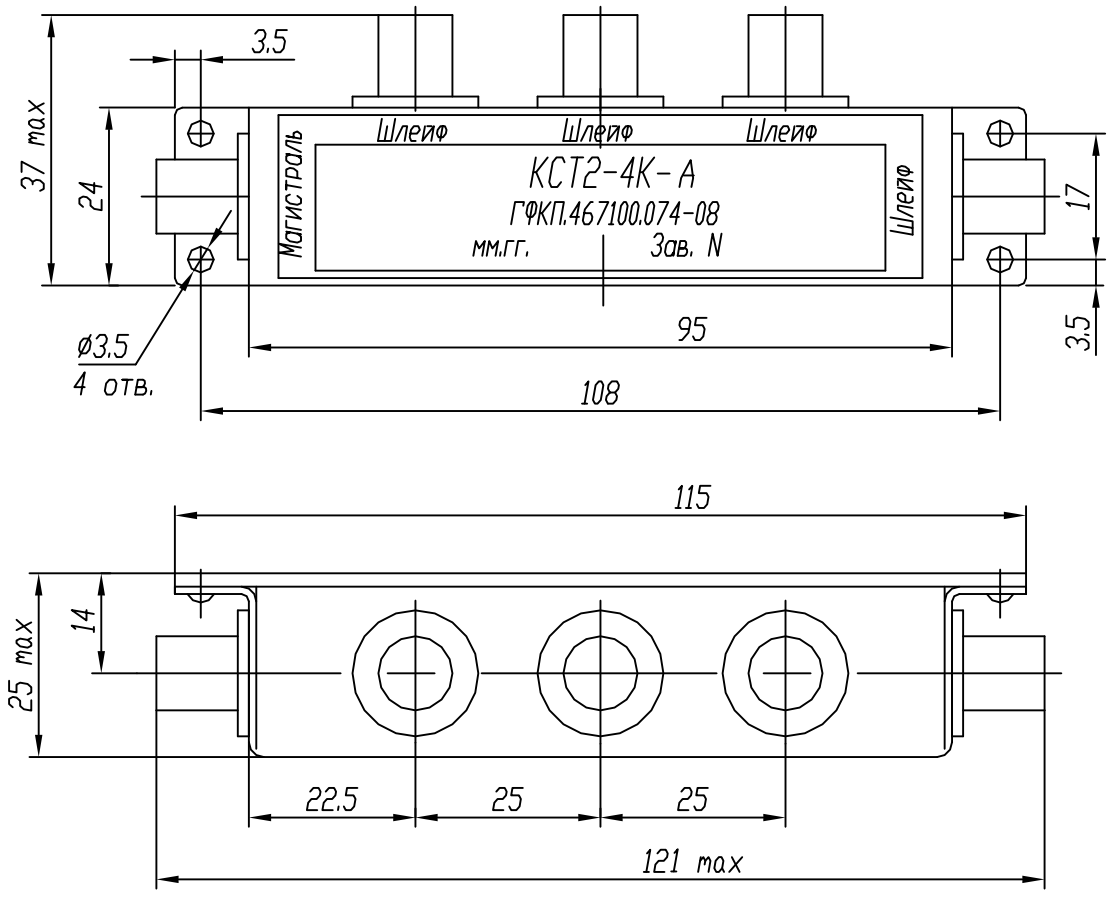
Габаритный чертеж коробки соединительной КСТ2-4К
